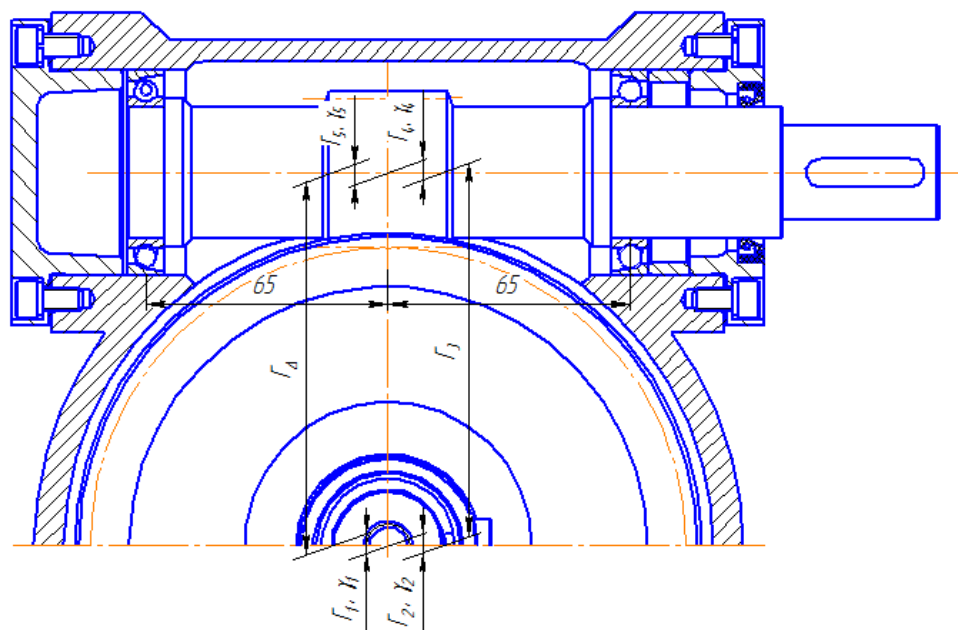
Червячный редуктор и схемы его размерных цепей
